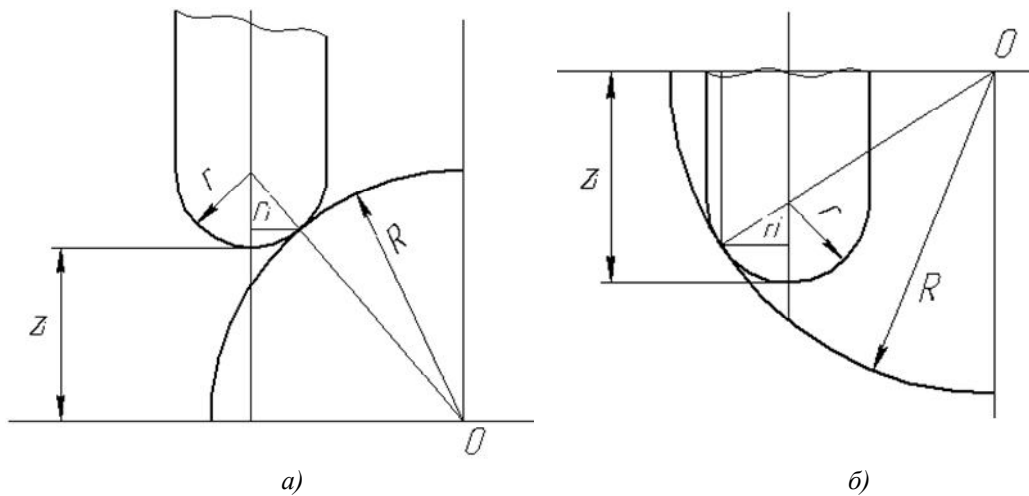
Фактичний радіус сферичної фрези в точці контакту з обробленою поверхнею
